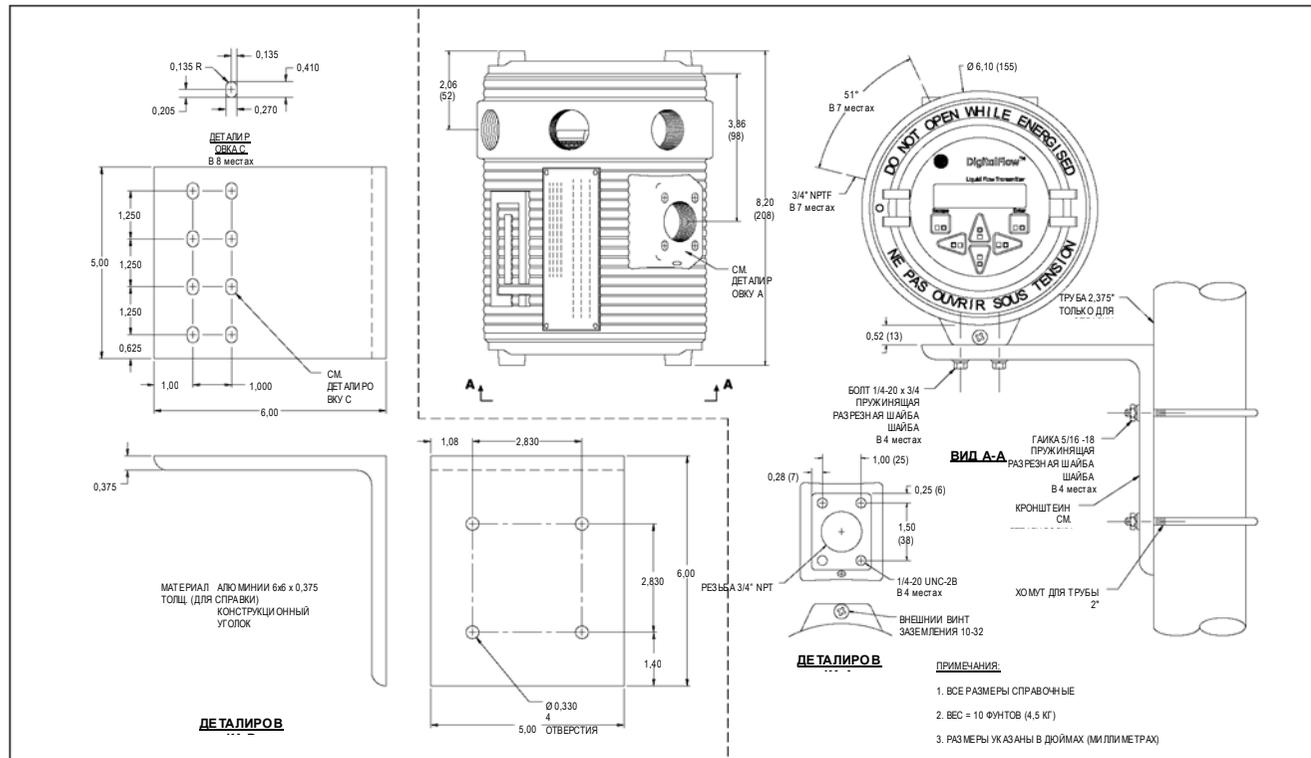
Эскизный чертеж и установка модели XGM868i – установочный кронштейн из уголка (ссылочный № чертежа 712-1317)
